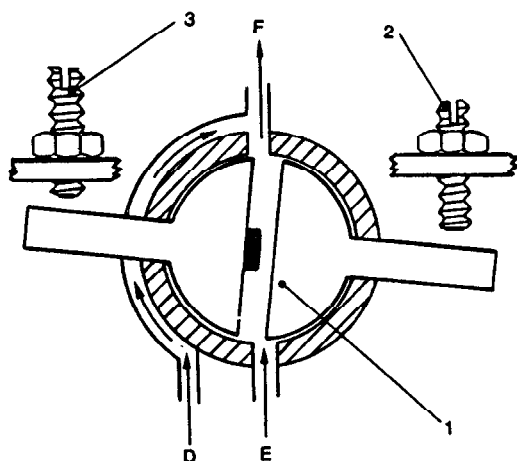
Válvula de paro: F combustible del acelerador, G combustible a los inyectores, 1 terminales, 2 válvula, 3 tornillo moleteado CUMMINS
